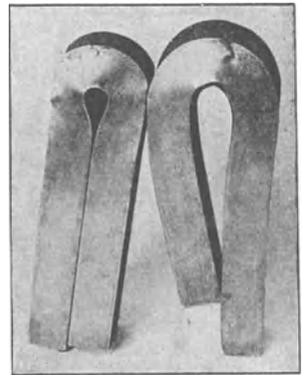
Biegeprobe von Schweißstäben.
